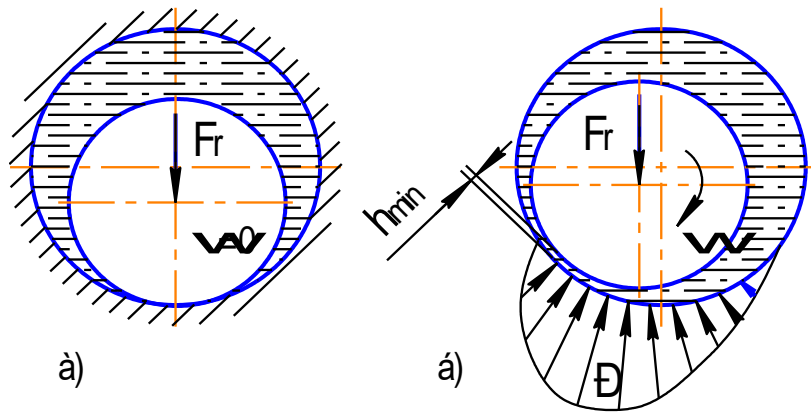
Положення вала в підшипнику й схема виникнення несучого мастильного шару
